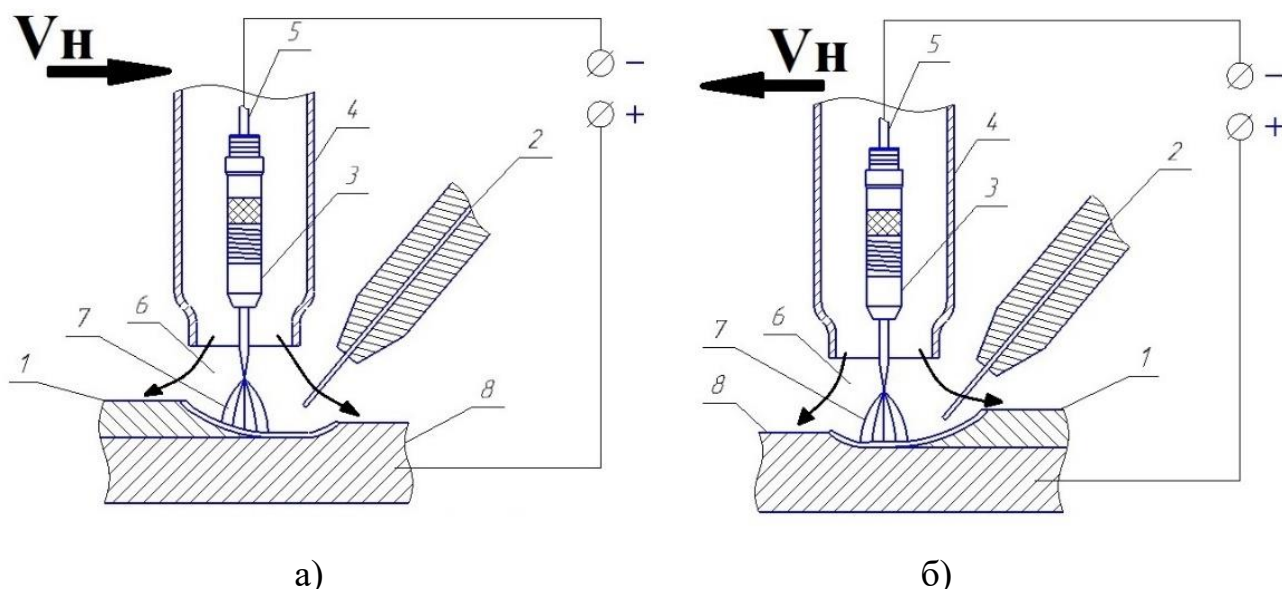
Схема процесса аргодуговой наплавки неплавящимся электродом: а) левый способ наплавки (проволока подается в головную часть сварочной ванны); б) правый способ наплавки (проволока подается в хвостовую часть сварочной ванны), где: 1 – наплавленное покрытие; 2 – присадочная проволока; 3 – сварочный диффузор; 4 – керамическое сопло; 5 – неплавящийся электрод; 6 – защитная газовая атмосфера; 7 – сварочная дуга; 8 – основной металл
